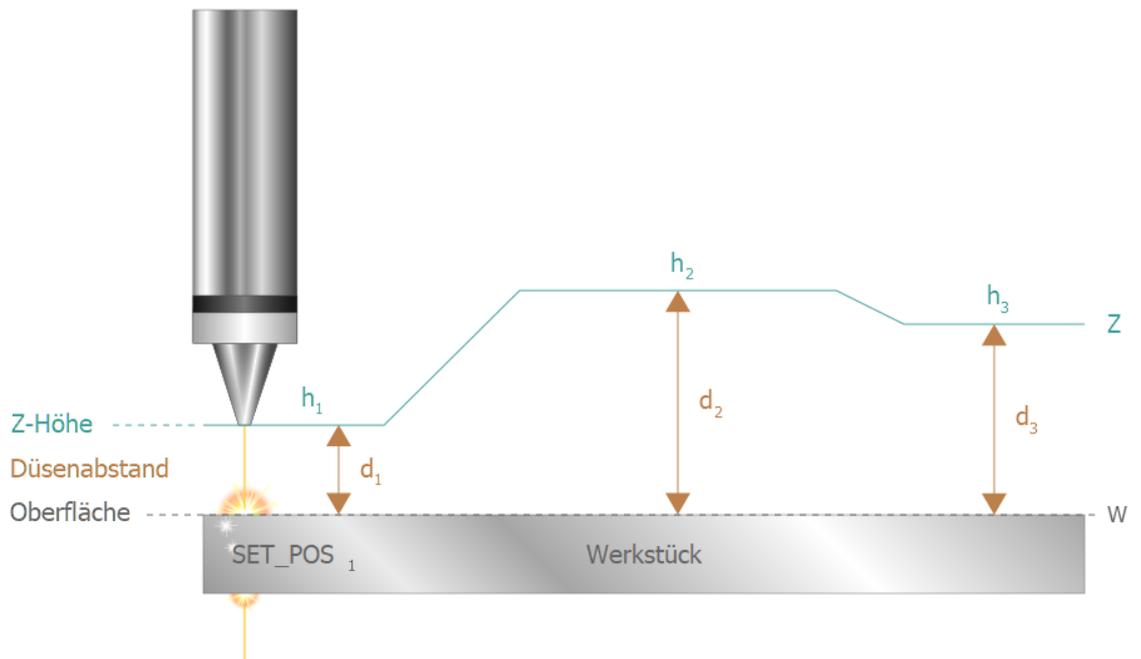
Konstante Werkstückoberfläche mit geändertem Werkzeugabstand
